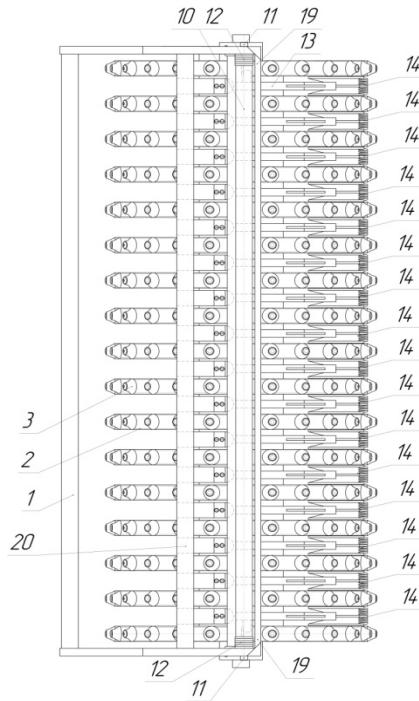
Вид сзади тандемного почвообрабатывающего катка
